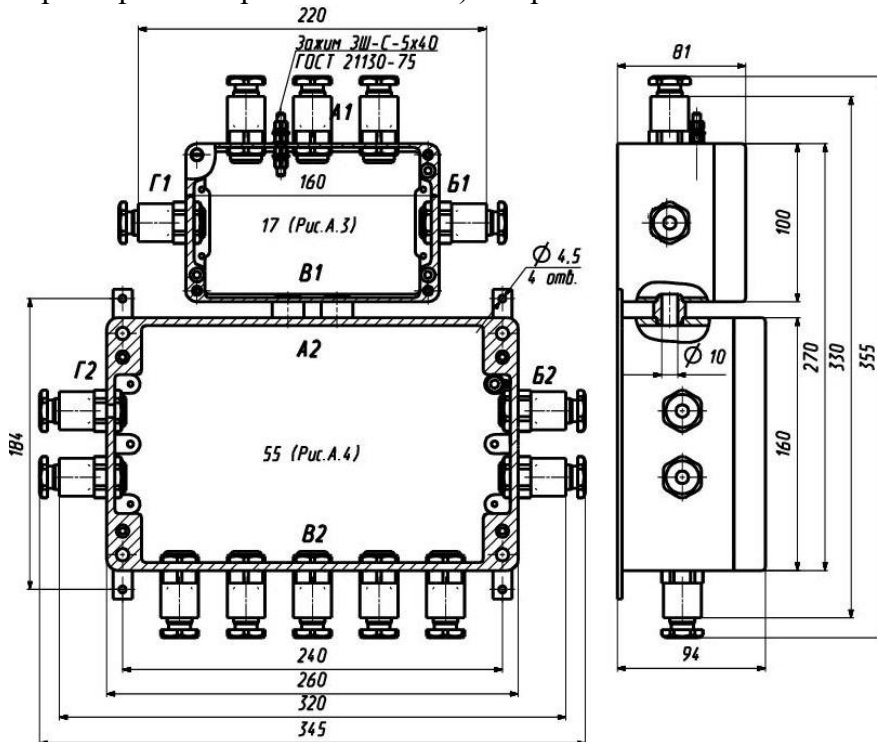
Блок корпусов и коробка клеммная ЕхБКО-А17В1/А55А2 (скрепление корпусов типоразмеров 17 и 55 сторонами В1 и А2) – вариант 4
